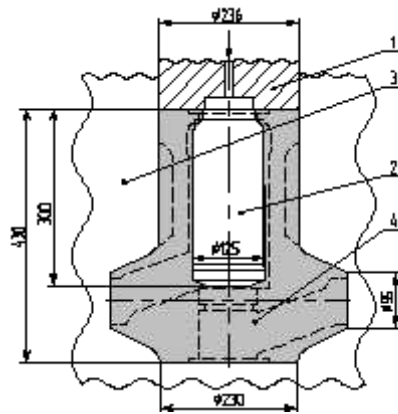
Схема штамповки корпуса типа тройника из стали 12Х18Н10Т:
